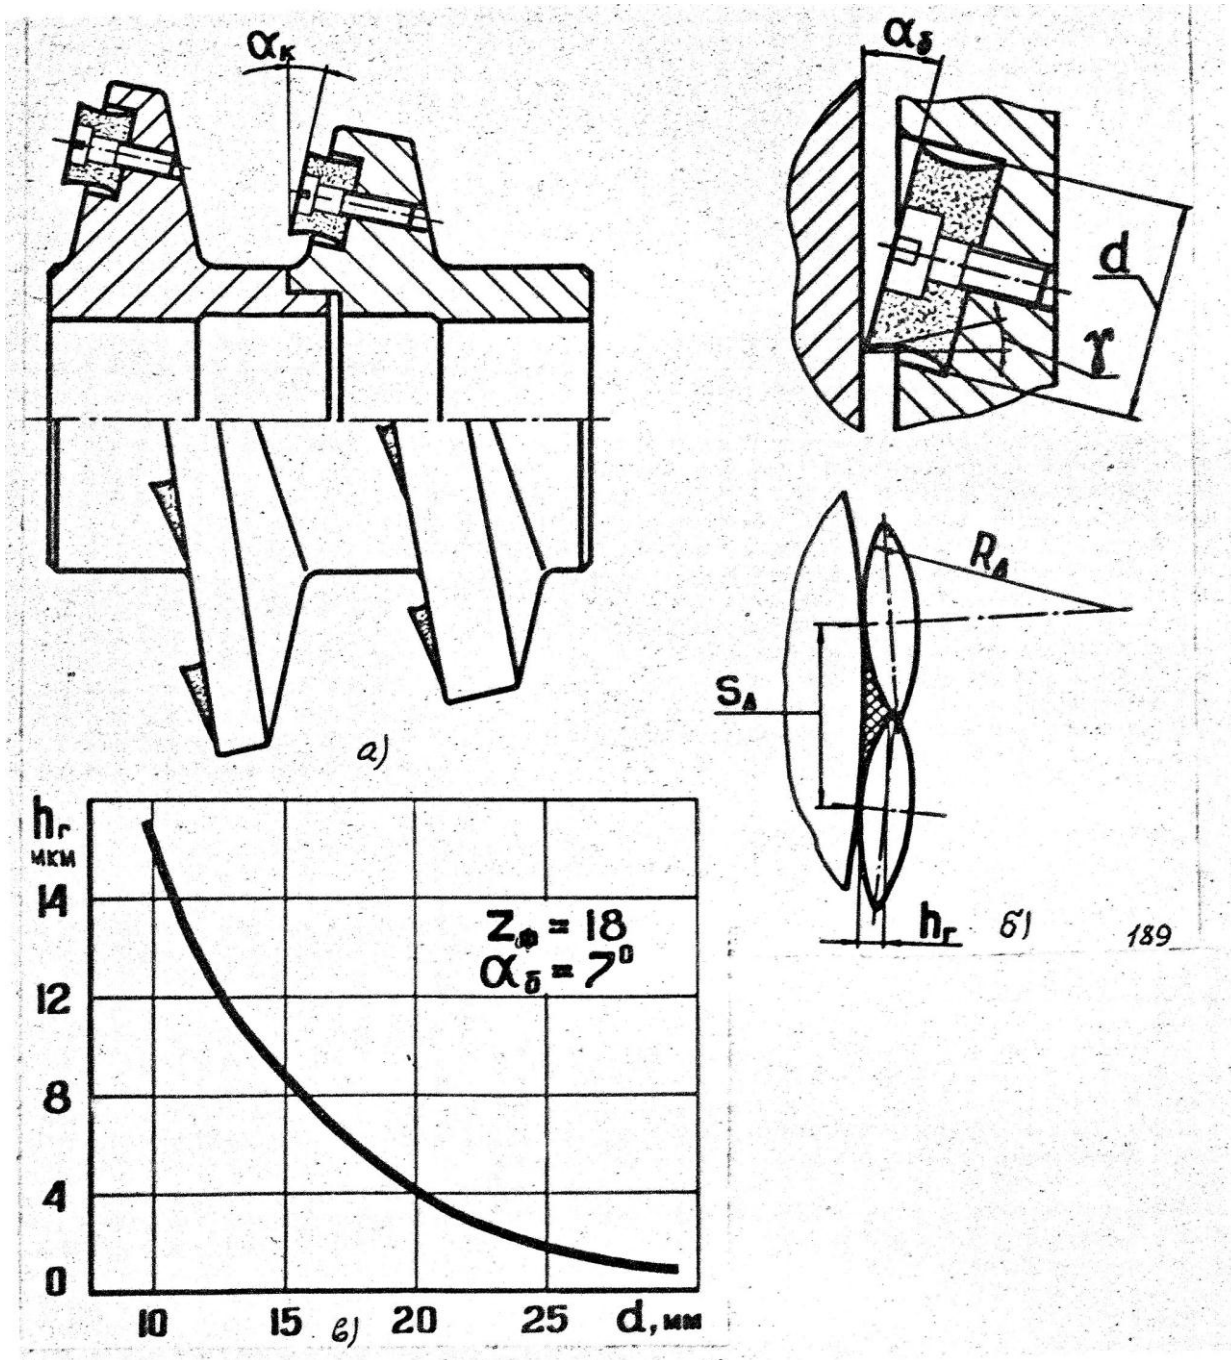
Червячная фреза с неперетачиваемыми режущими элементами-роликами: а – общий вид правого корпуса фрезы; б – образование гребешка неровности в процессе обкатки зуба колеса; в – зависимость высоты неровностей от диаметра режущего элемента-ролика
